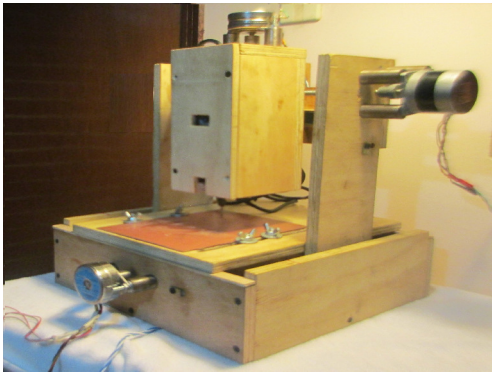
Estructura de la máquina fresadora CNC para elaborar PCB's.
